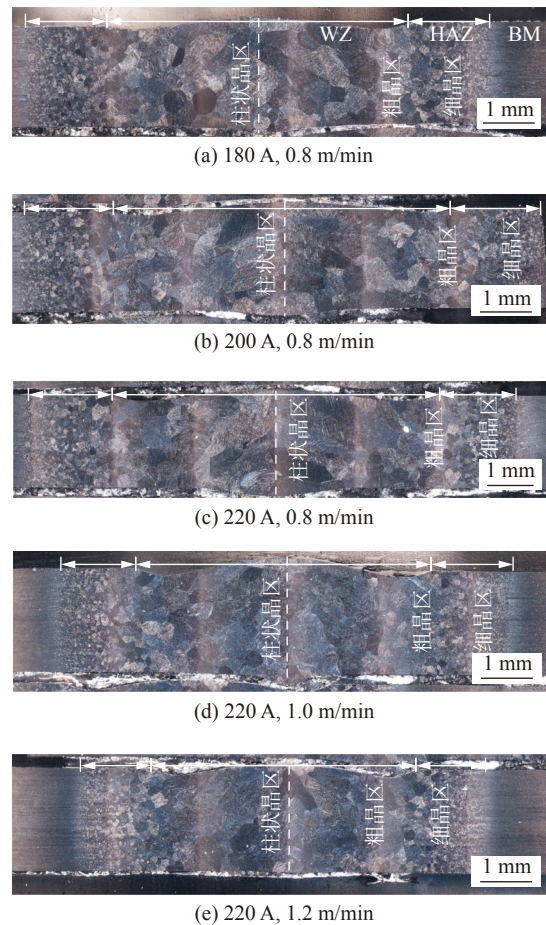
不同 TIG 焊接参数下的焊缝横截面形貌
